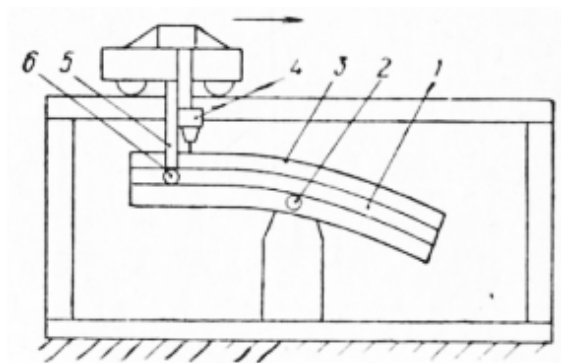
Установка для сварки по копиру продольного криволинейного шва:
